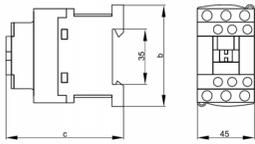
Габаритные размеры контакторов ПК-106XX - ПК-118XX
